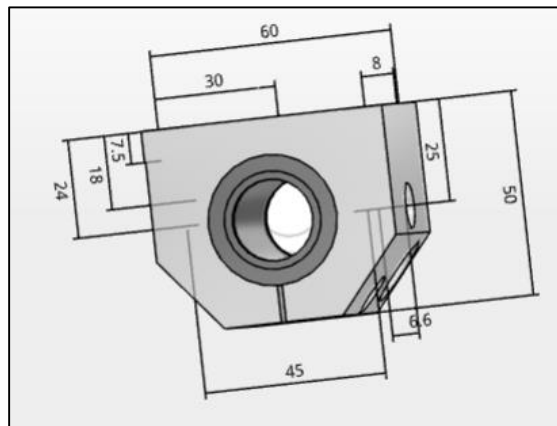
Dimensiones del rodamiento lineal utilizado
